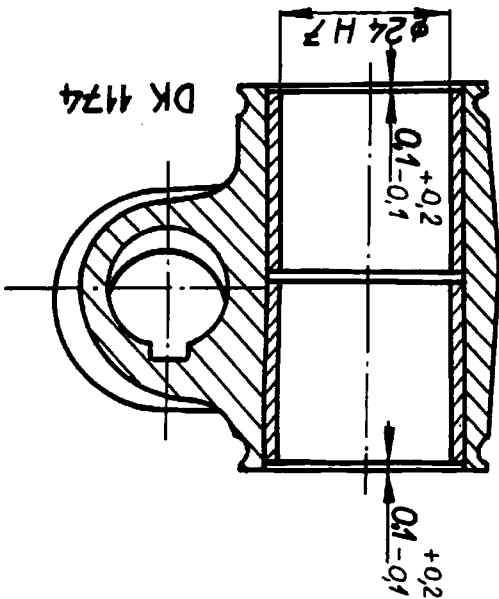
/1 Lenkanschlagköpfe — Abmessungen für Einpressen und Bearbeitung der Buchsen
